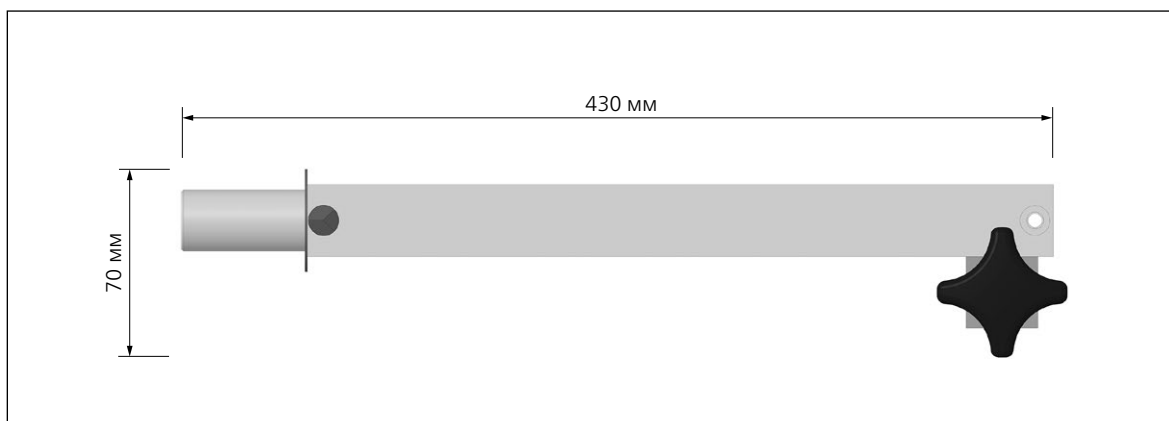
Устройство HV 207, вид сверху, размеры в мм
